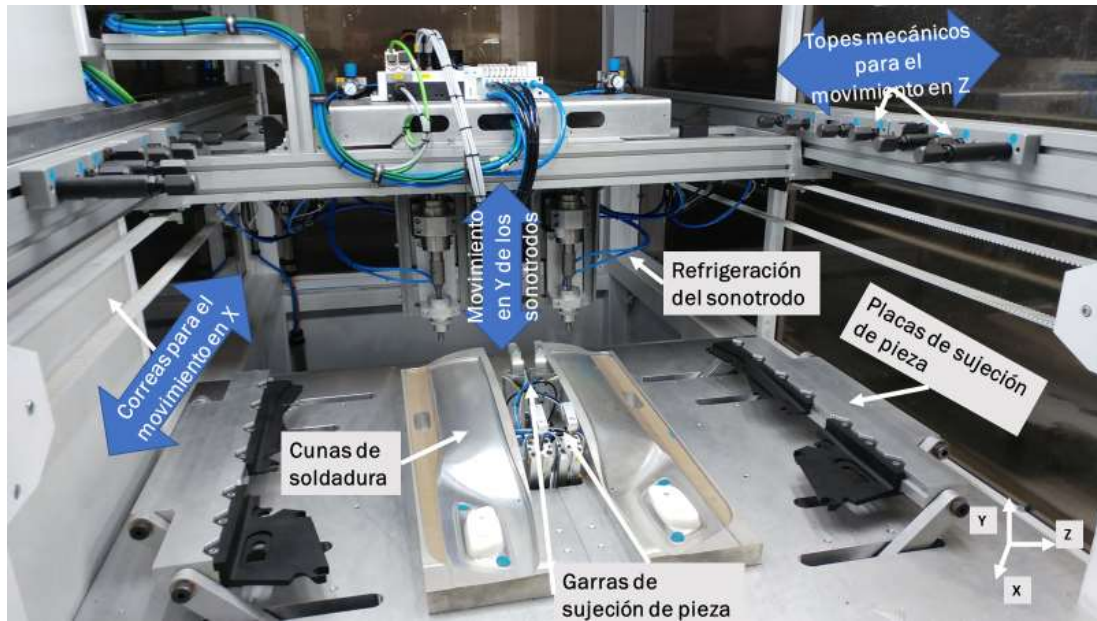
Esquema básico de la máquina de soldadura Bocanegra. Fuente: Elaboración propia
